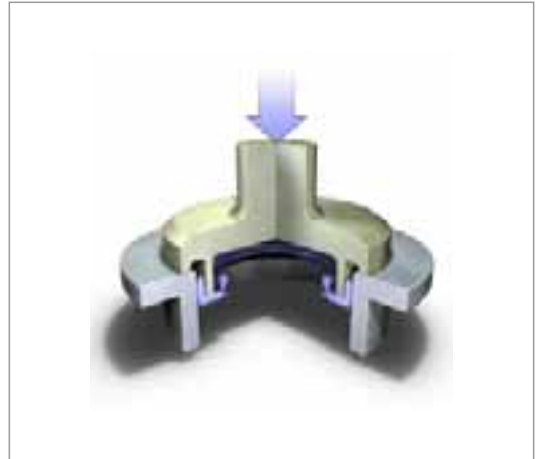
Montage Bodenseite voraus. Außendurchmesser des Montagedorns ca. 0,5 mm kleiner als der Innenaussenkungsdurchmesser der Dichtung. Im Bedarfsfall bei uns zu erfragen.
